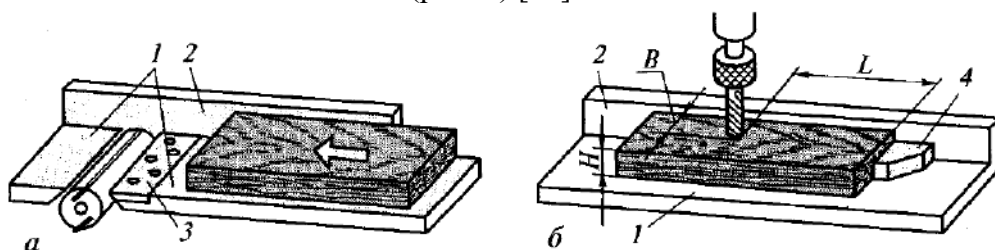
Рухоме а) та нерухоме б) базування заготовок при деревообробці [10]:
